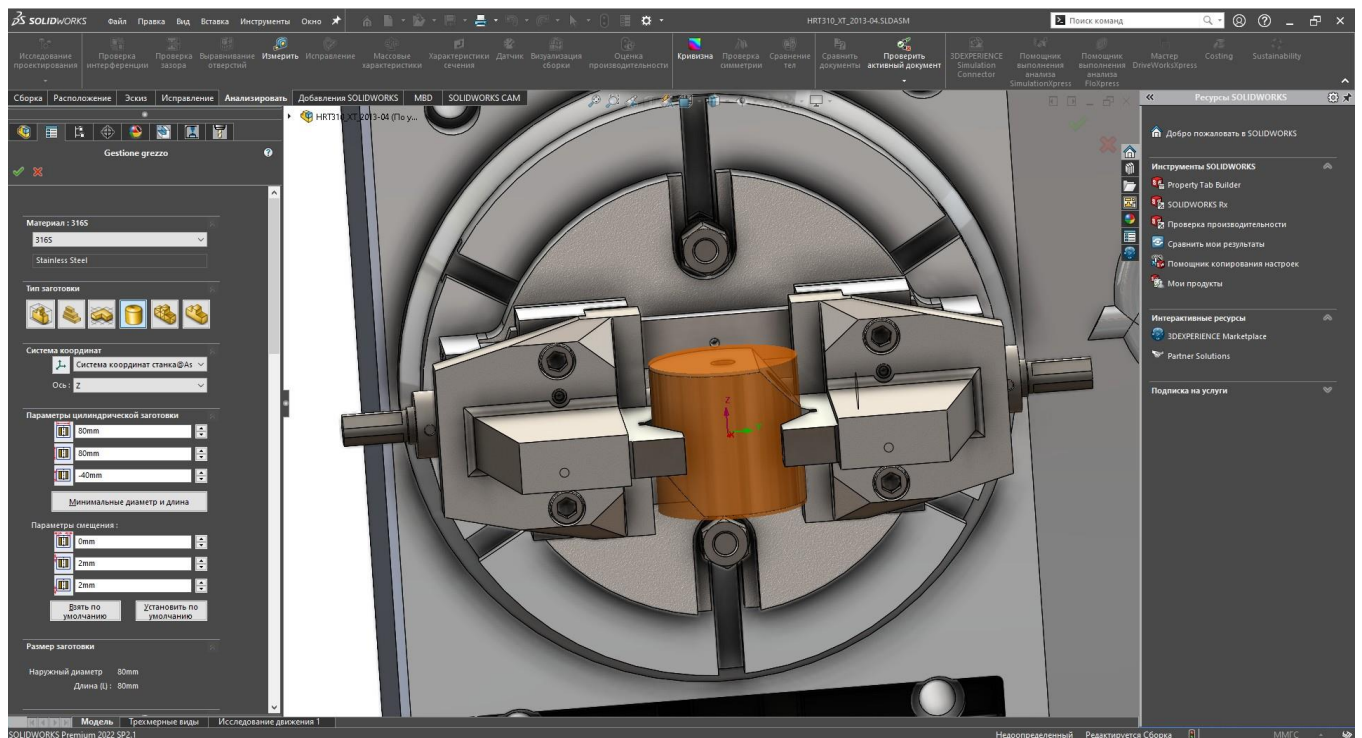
Тривимірна схема закріплення заготовки
